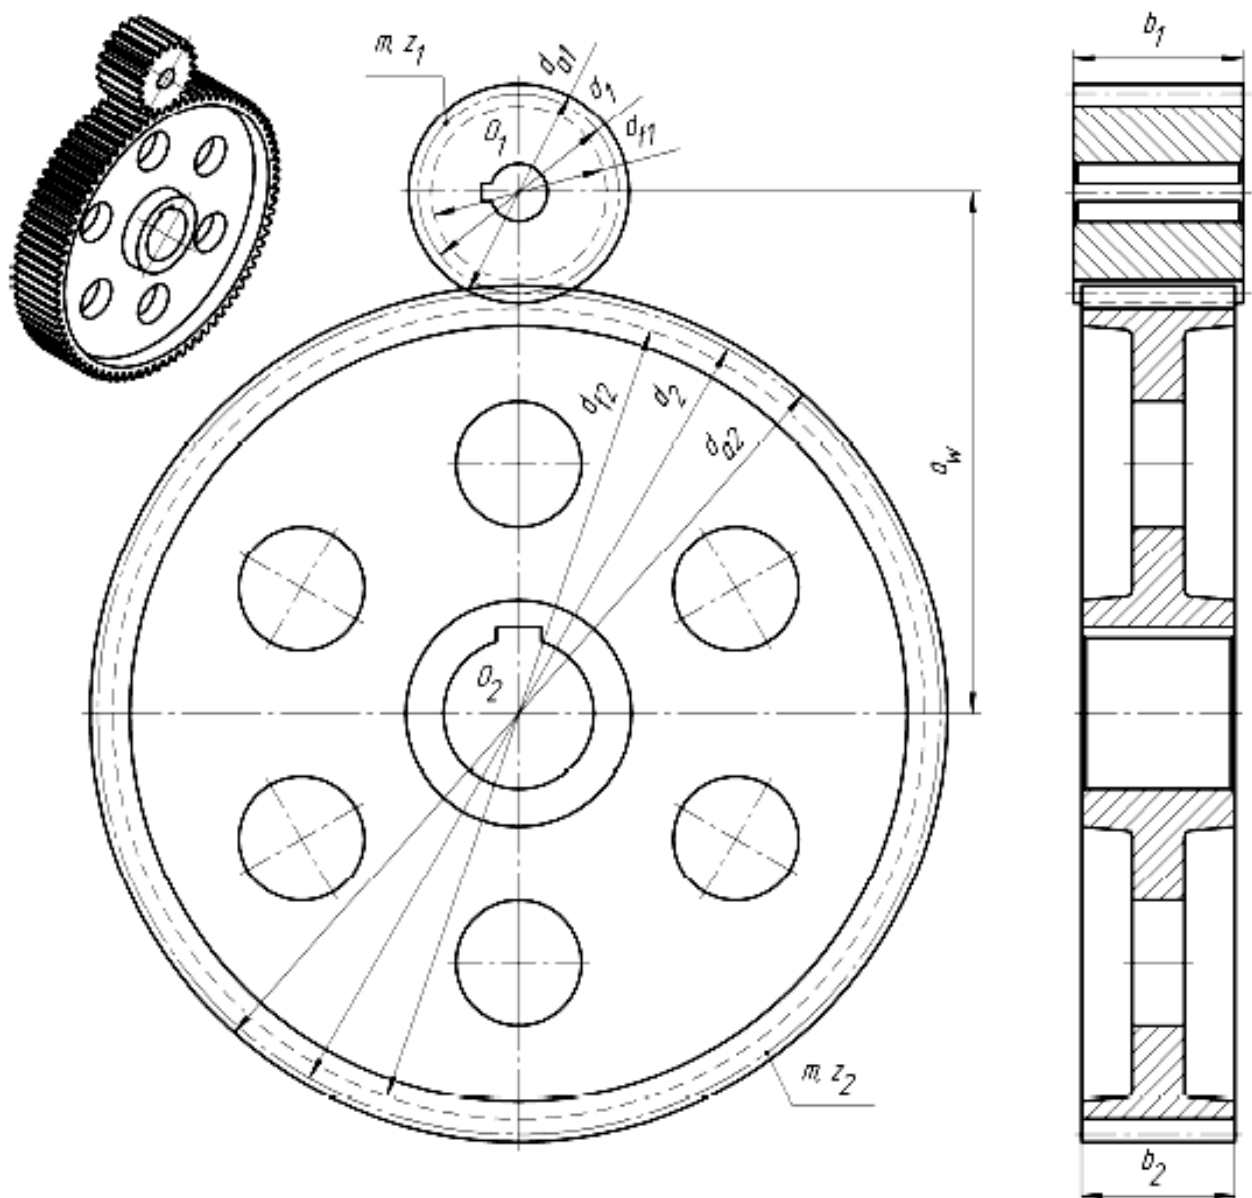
Циліндрична зубчаста передача редуктора
